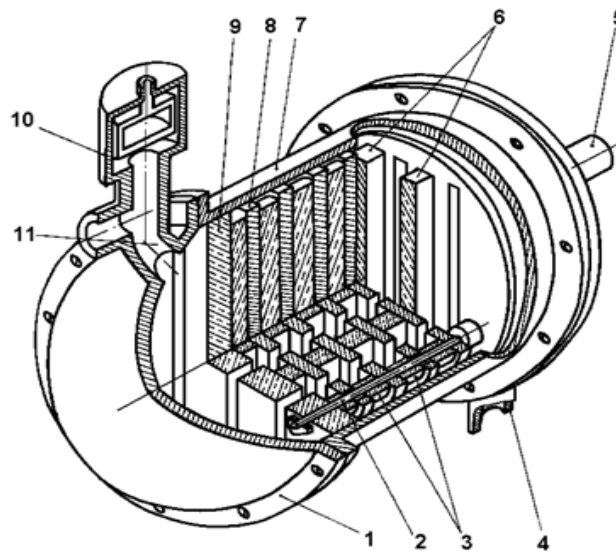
Конструкція електричного очищувача діелектричних рідин: 1 - кришка; 2 - стяжна шпилька; 3 - прокладки; 4 - патрубок зливу рідини; 5 - патрубок входу; 6 - патрубок виходу; 7 - корпус; 8 - електродні пластини; 9 - діафрагма; 10 - гідравлічний поплачковий клапан; 11 - патрубок виходу очищеної рідини
